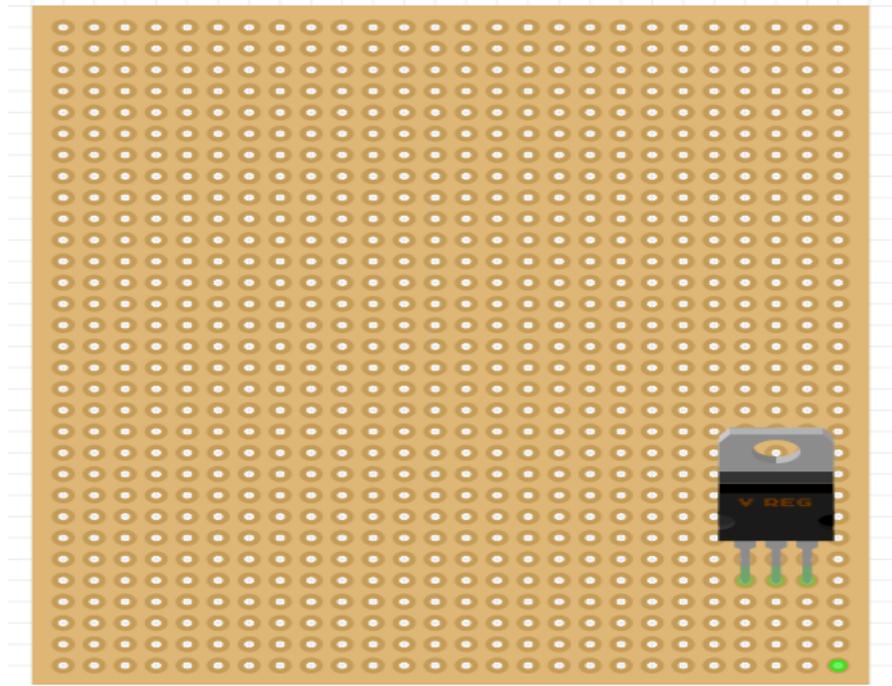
L'emplacement du régulateur dans la plaque trouée.
